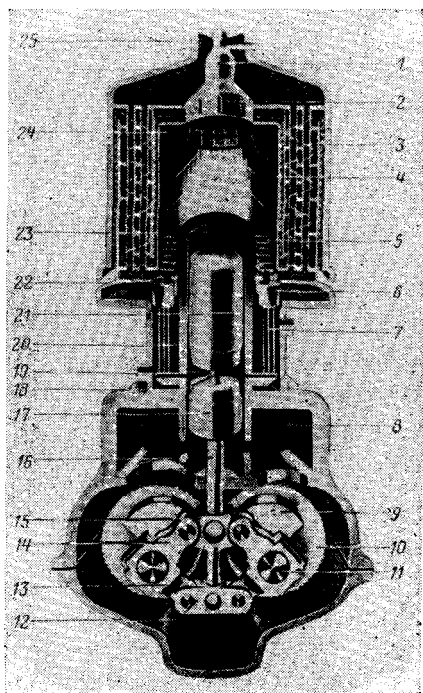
Схема одноцилиндрового вытеснительного типа двигателя Мейера с ромбическим приводом.
